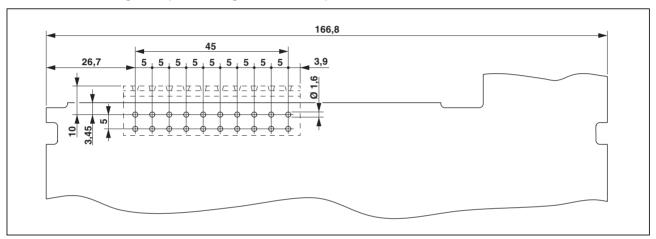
Maßzeichnung der Leiterplatte des Gehäuses bei Verwendung des Anschlusstechnik-Trägers CT20
